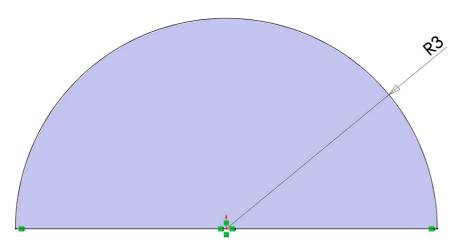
Эскиз детали 1, части 2: шарик подшипника
